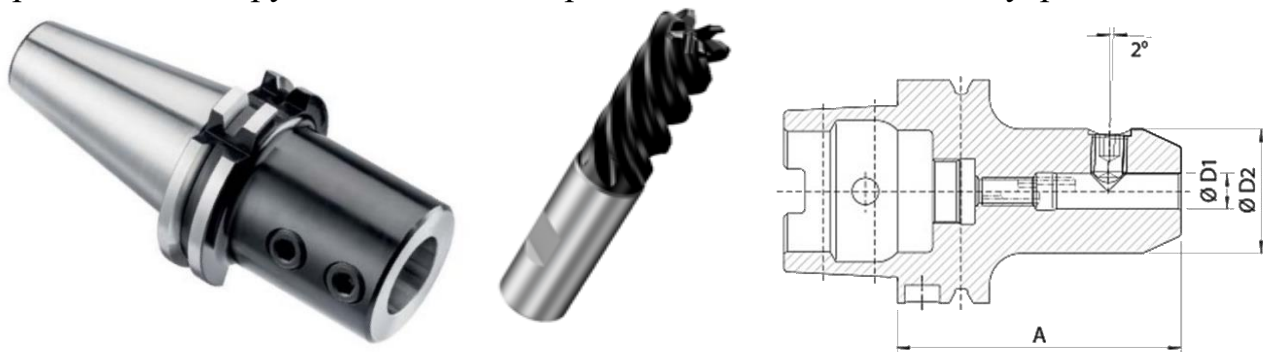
Внешний вид патрона Weldon (слева) и инструмент с соответствующим хвостовиком (в центре); устройство патрона Whistle Notch (справа)
